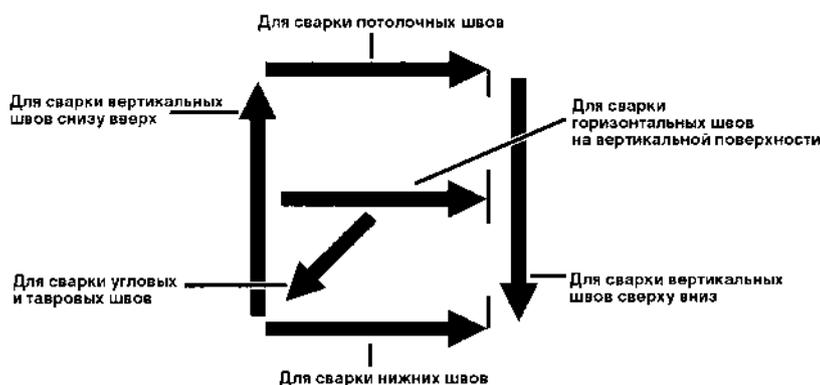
Графическое изображение пространственных положений сварки и наплавки
